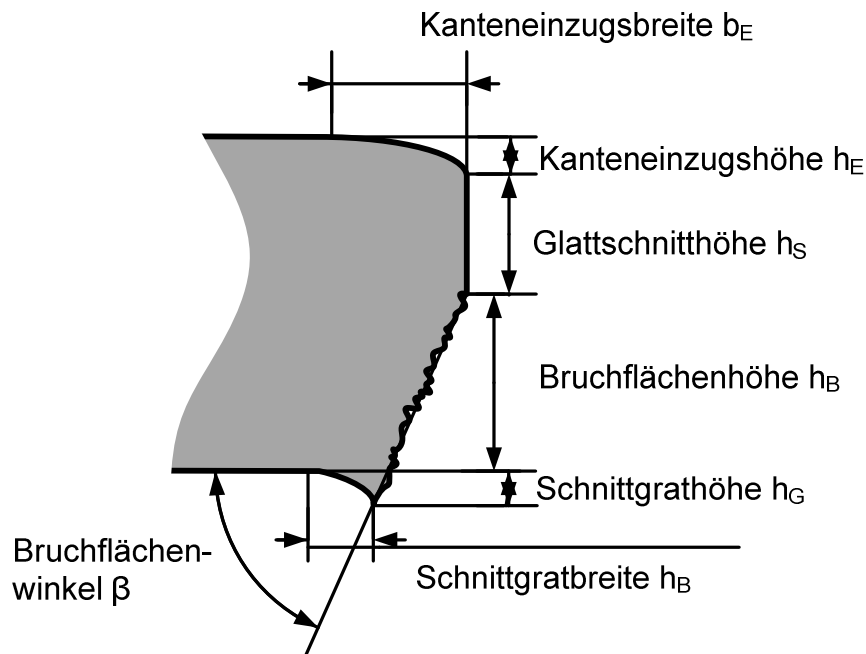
Schnittfläche nach VDI 2906 mit Schnittflächenkenngrößen
